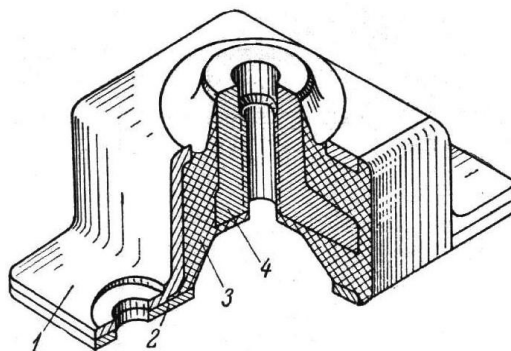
Сварные резинометаллические виброизоляторы
